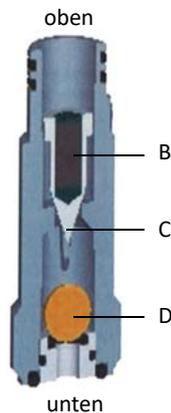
Querschnitt Kugelrückschlag-Gehäuse
